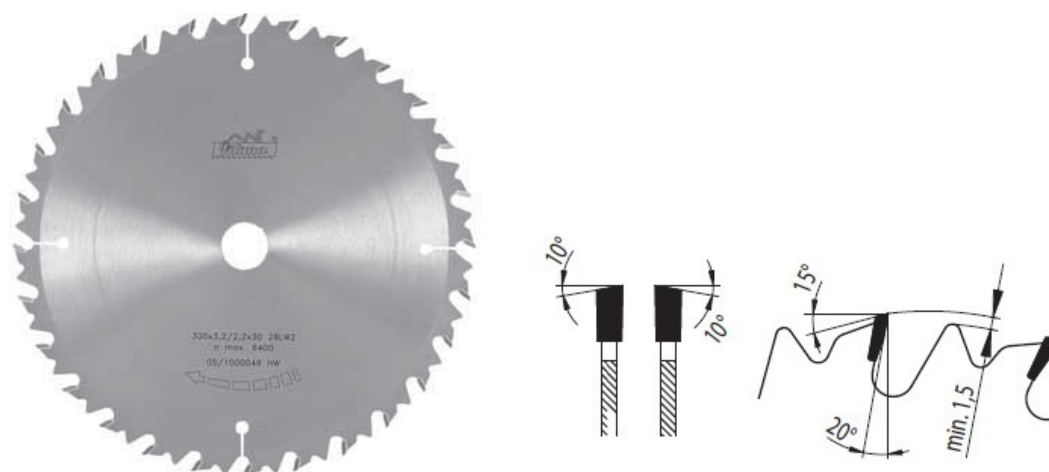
Rozmítací pilový kotouč (Pilana, 2011)
